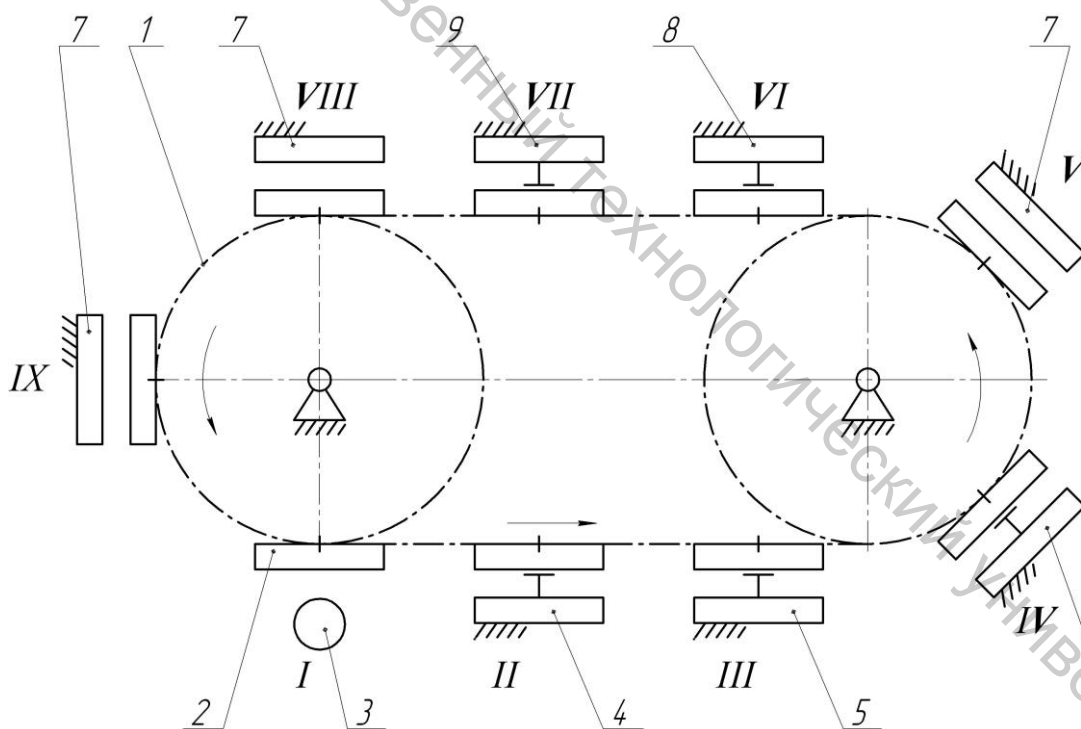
Технологическая схема агрегата контурной обработки подошв АКОП-9: 1 – цепной транспортер, 2 – каретки (всего 9), 3 – оператор, 4, 5, 6, 8, 9 – обрабатывающие головки, 7 – установки для сушки (всего 3), позиции: I – загрузка-выгрузка, II – фрезерование контура подошв, III – увлажнение, IV – нанесение мыльной эмульсии, V – подсушка, VI – уплотнение, VII – покраска торца, VIII, IX – сушка
